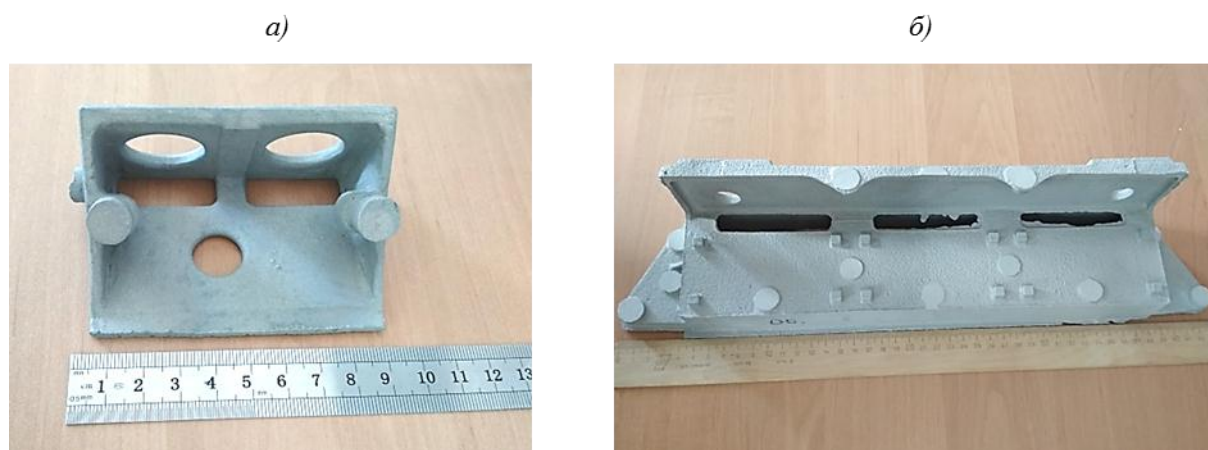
Отливки типа «Кронштейн» (а) и «Корпус» (б) из литейного алюминиевого сплава АК7ч.
